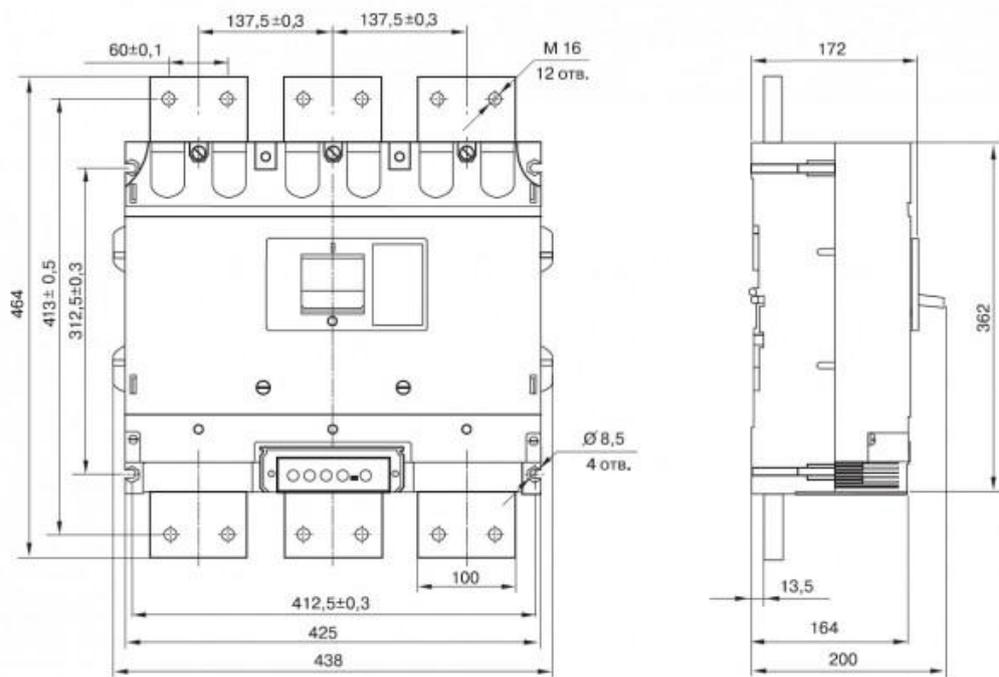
Вид с боку и габаритные размеры выключателя ВА 3736 1600А
